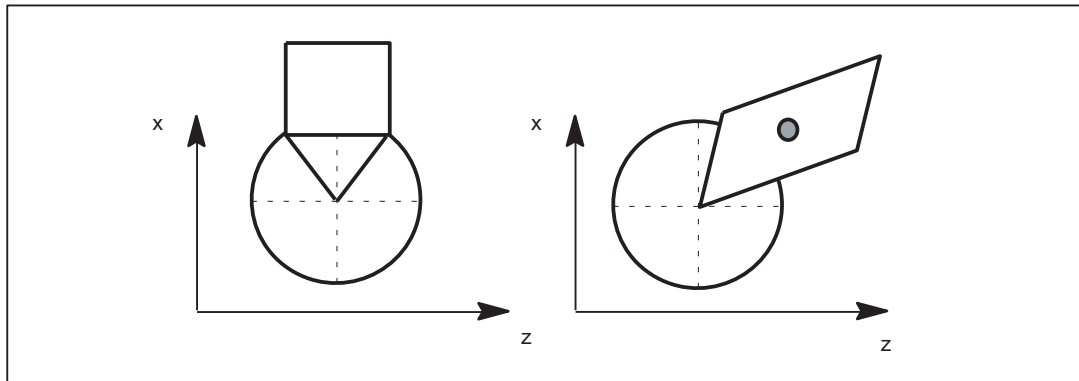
Messen von Werkzeuglängen mit Lupe
